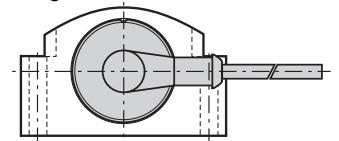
Maßzeichnung (Wegaufnehmer BTL6...A1-S115 mit Positionsgeber BTL5-A-3801-2 und Befestigungsklammern BTL6-A-MF03-K-50)
